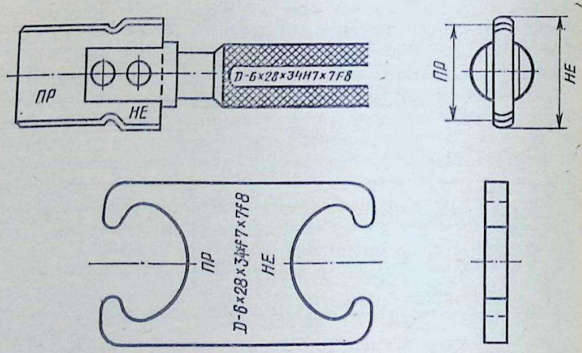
Специальные калибры для поэлементного контроля шлицевых поверхностей.
